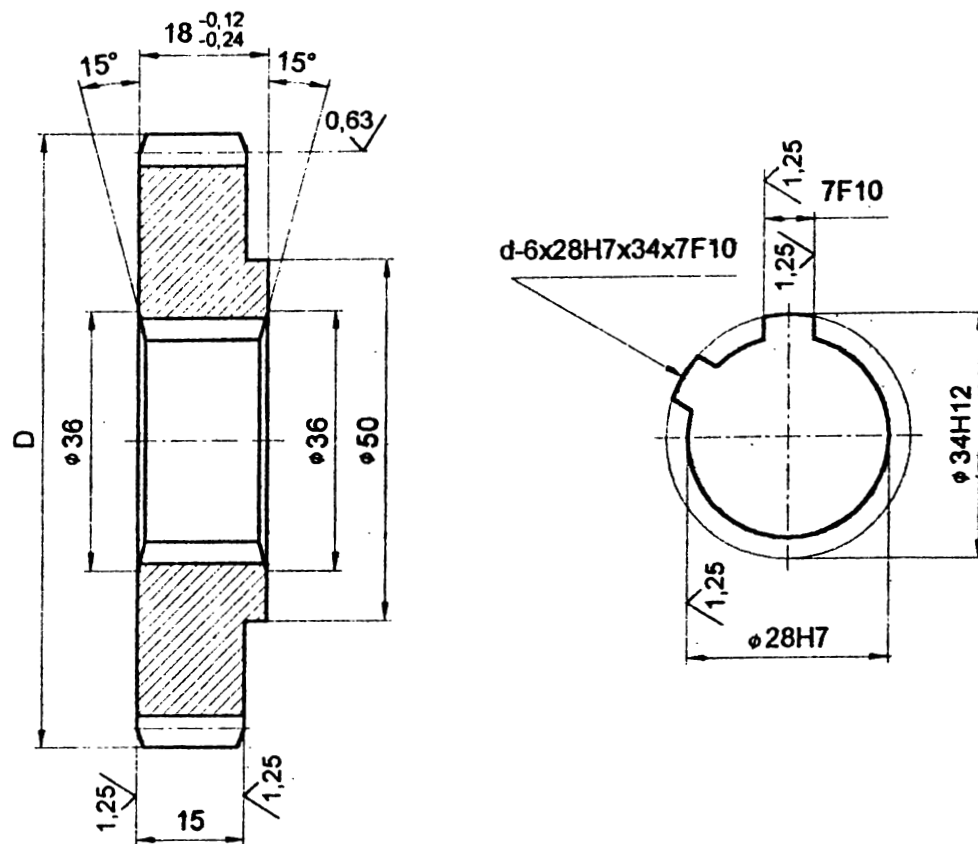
Типовой чертеж сменного зубчатого колеса
